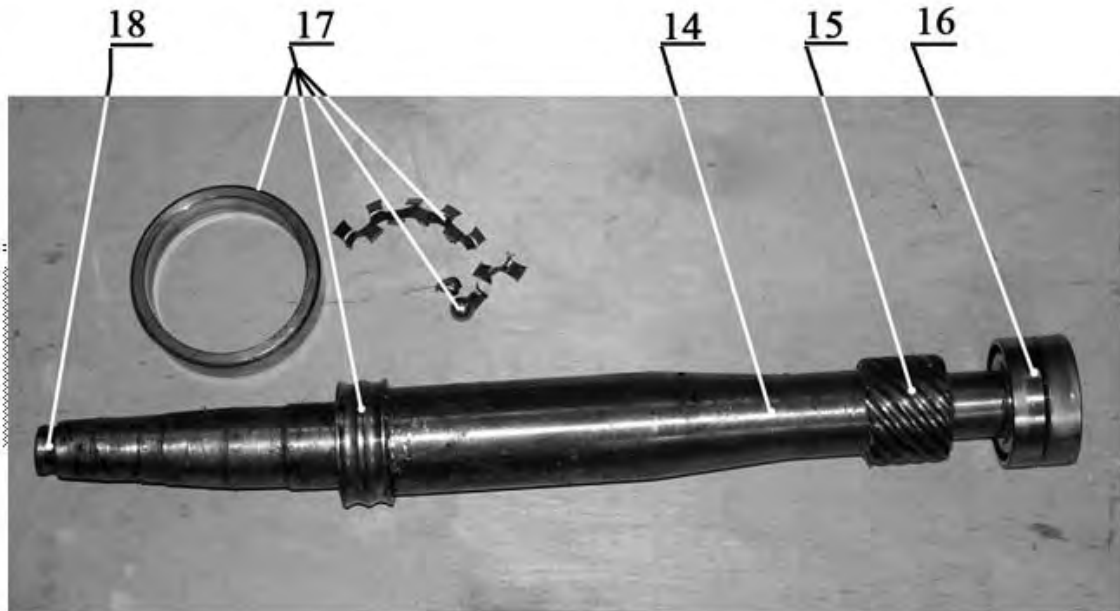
Вид поврежденного вертикального вала с подшипниковыми опорами
